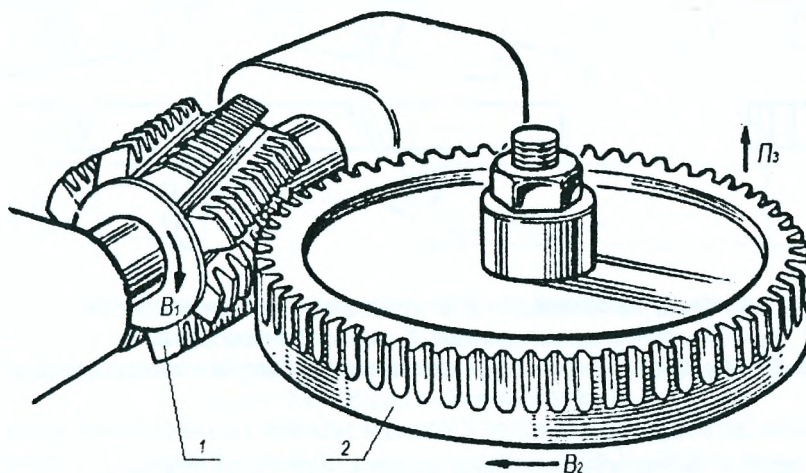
Схема нарезания цилиндрического зубчатого колеса
